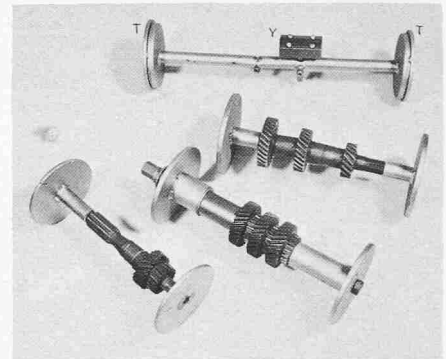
B. Einspannvorrichtungen für die Durchschleusung von Stirnrädern, Vorgelegewellen und ähnlichen Teilen durch mit Längswalzen ausgerüstete Durchlaufmaschinen gemäss Arbeitsprinzip Bild 20A. In diesen Maschinen wird auch eine ähnliche Hilfsvorrichtung für den Durchlauf eines Almen-Test-Einspannblocks samt Prüfplättchen zwecks Messung der Strahlintensität benötigt. Eine solche ist im Bild als Position T - T zu oberst zu sehen, wobei der Aufspannblock für das Almen-Testprüfplättchen mit Y gekennzeichnet ist. Photo: Graber und Wening AG, Neftenbach
